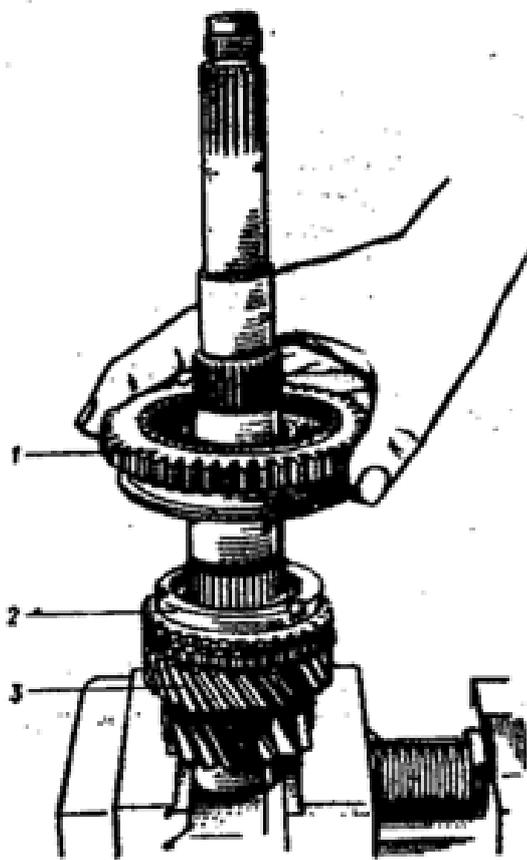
Снятие ступицы третьей и четвертой передач с ведомой шестерней заднего хода: 1 - шестерня ведомая заднего хода; 2 - кольцо синхронизатора; 3 - шестерня ведомая четвертой передачи
